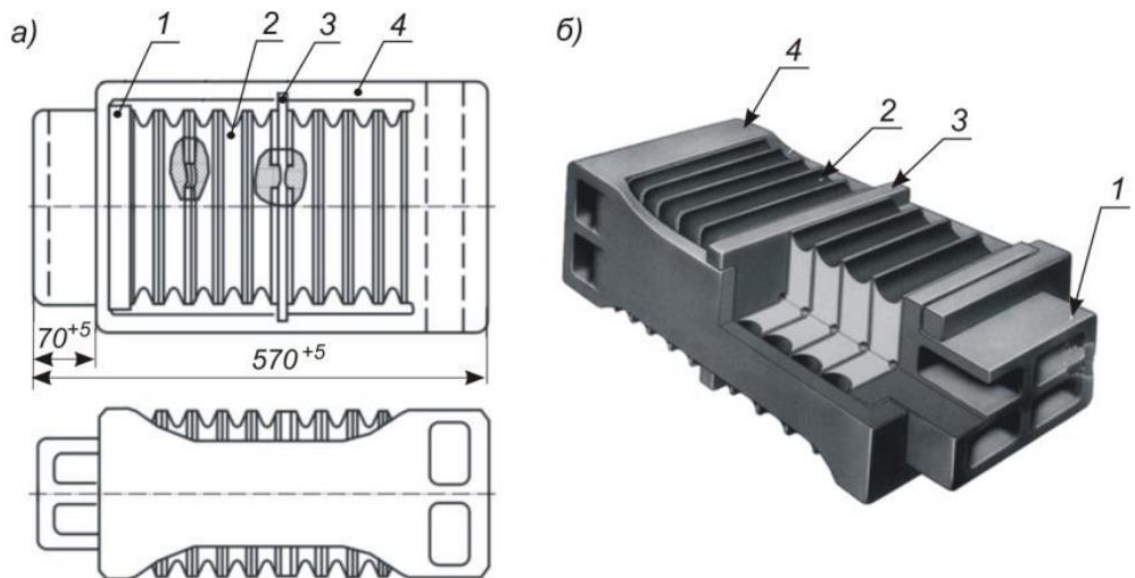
Загальний вигляд ПА типу Р-2П
